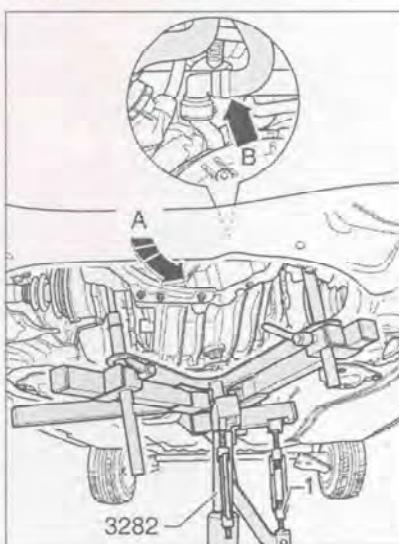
С помощью болта (1) приспособления 3282 поверните коробку передач вправо и вниз (стрелка А).
